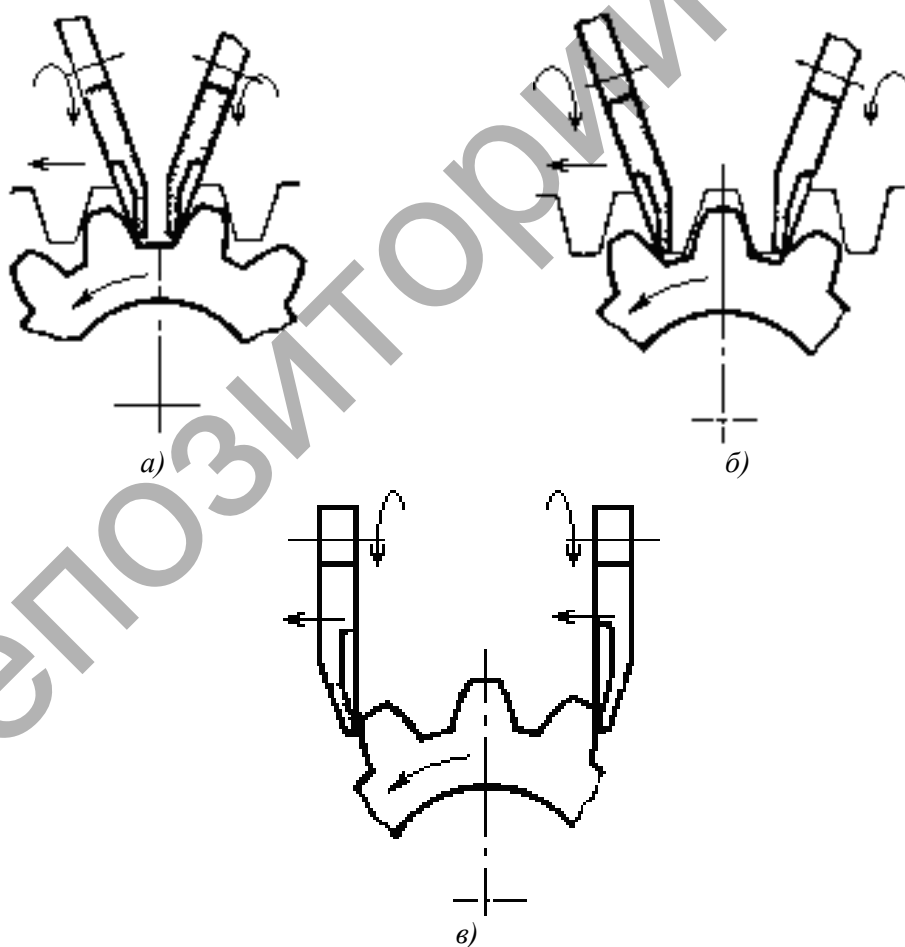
Схема шлифования зубчатых колес тарельчатыми кругами и схемы их установки
